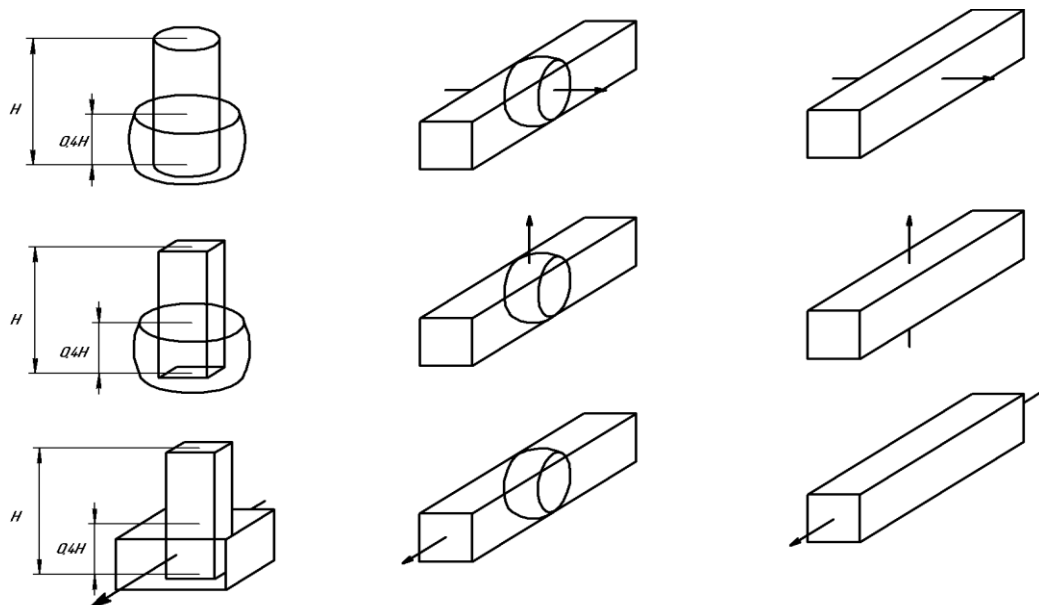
Схема БИПД всесторонней ковкой
